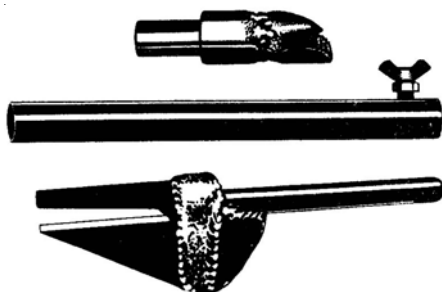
Инструменты, изготовленные по типу консервного ножа
